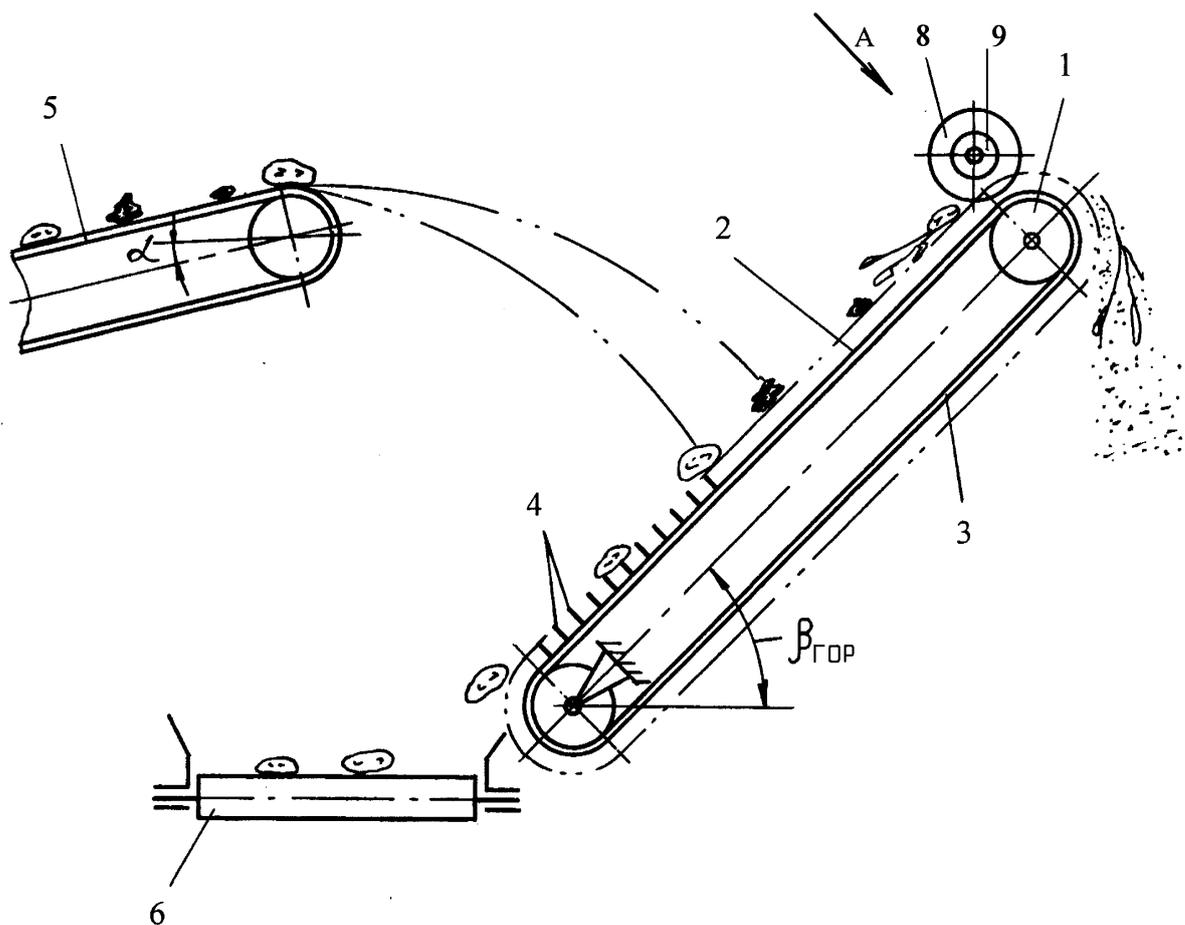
Пальчатая горка картофелеуборочной машины Grimme DR1500 и подпружиненные отбойные пластины
